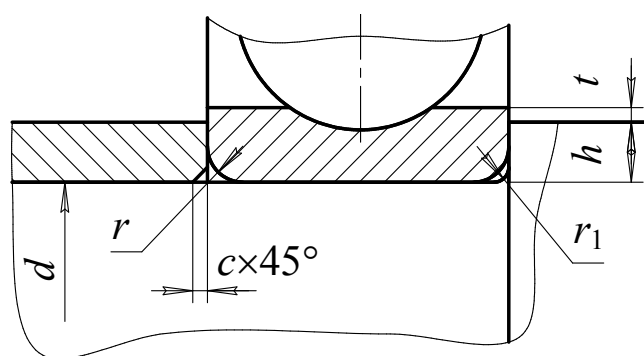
Уступ вала возле торца подшипника качения
